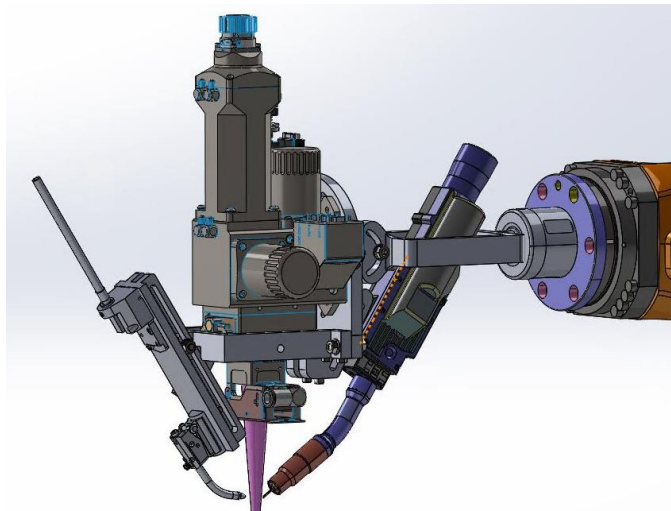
12 Sistema de herramientas de soldadura montadas en el cabezal (2)
